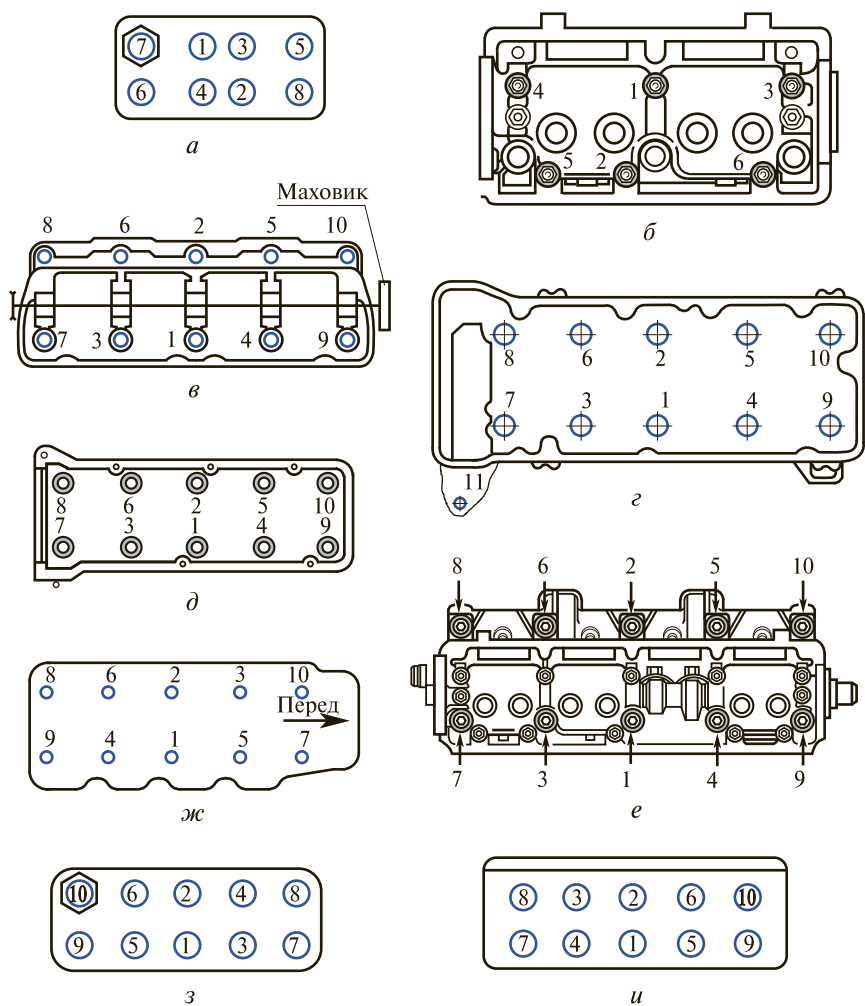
Порядок затяжки гаек (болтов) крепления головок цилиндров двигателей:
